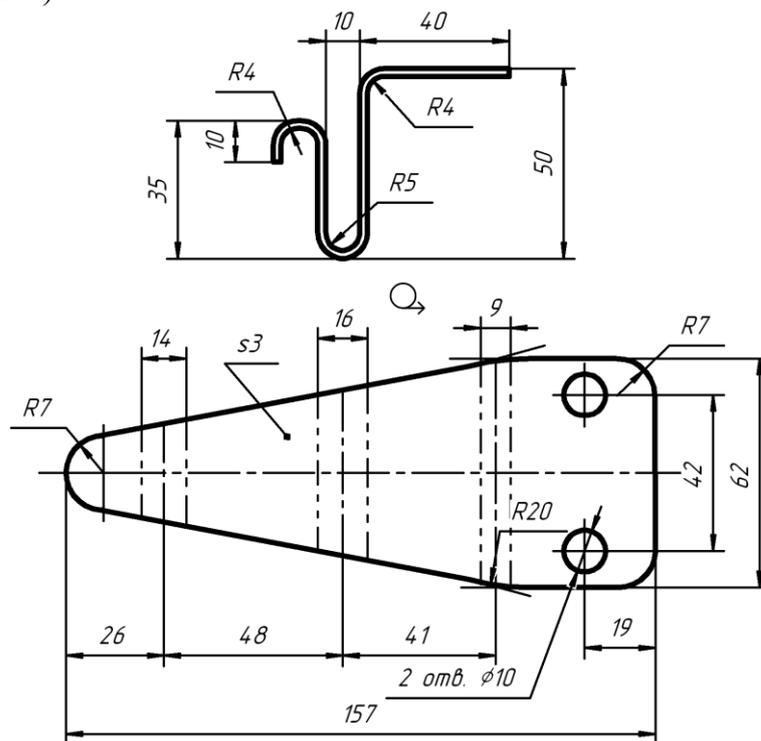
Чертеж фасонной листовой детали с разверткой
